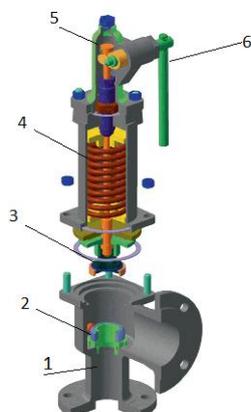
Пружинный предохранительный клапан с фланцевым присоединением (1) и устройством ручного открытия клапана (6)
